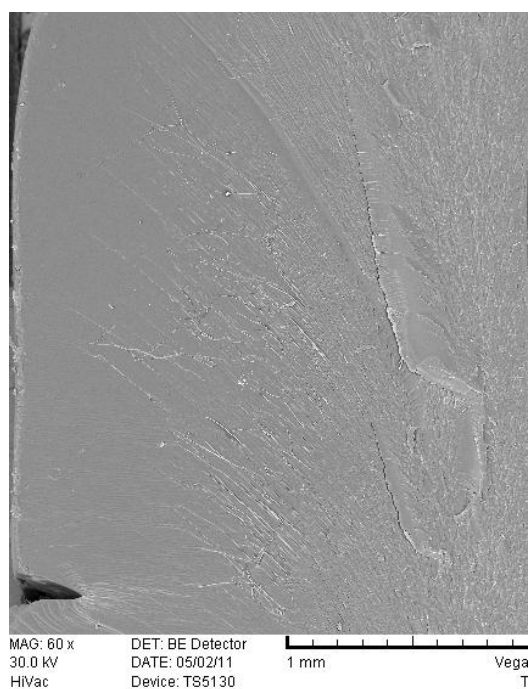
Detailní pohled na lom vzorku s tloušťkou 7,5 mm 1x sycený
